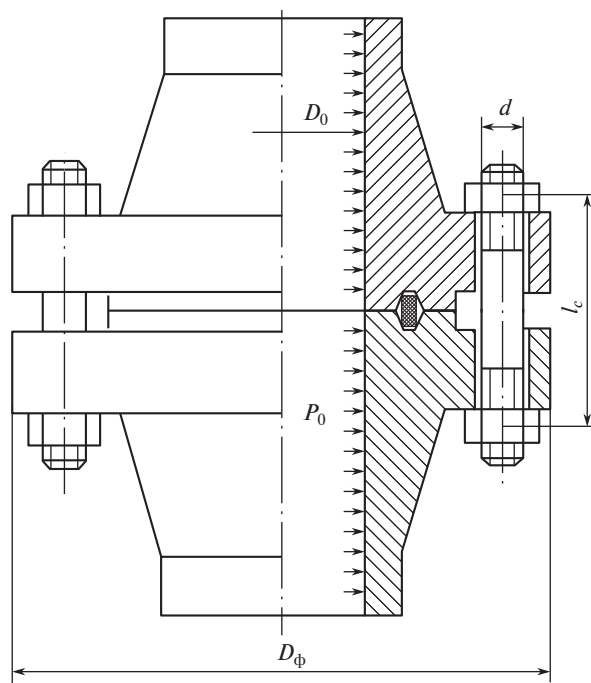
Уплотнитель фланцевого соединения высокого давления: P_0 — внутреннее давление; D_0 — внутренний диаметр фланца; D_ϕ — внешний диаметр фланца; l_c — длина болта.
